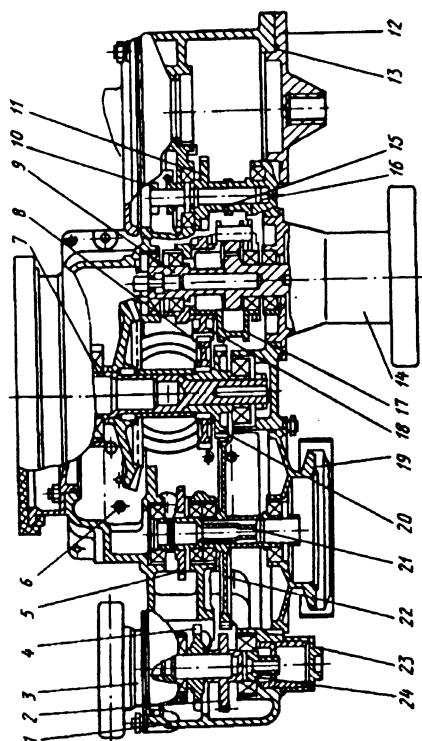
Коробка приводов (горизонтальный разрез);
